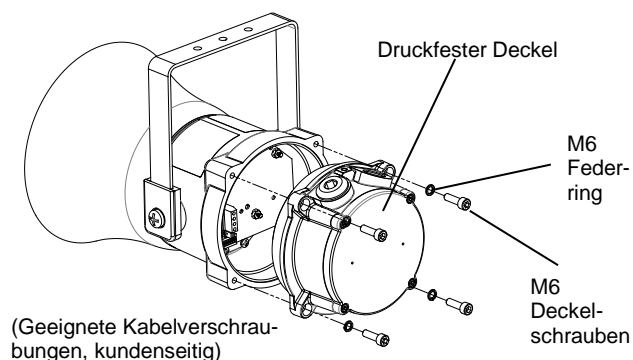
A Zugang zum explosionsgeschützten Gehäuse
